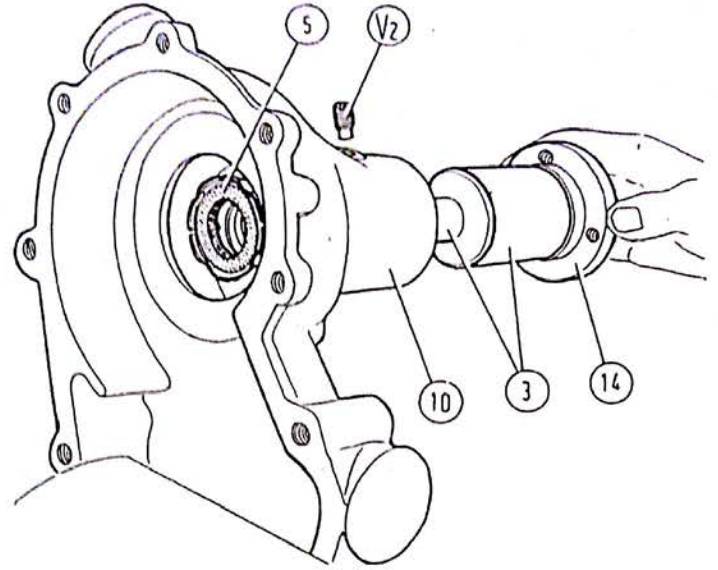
/13 - Démontage (Remontage) de l'arbre de commande (3) et du moyeu de ventilateur (14).
